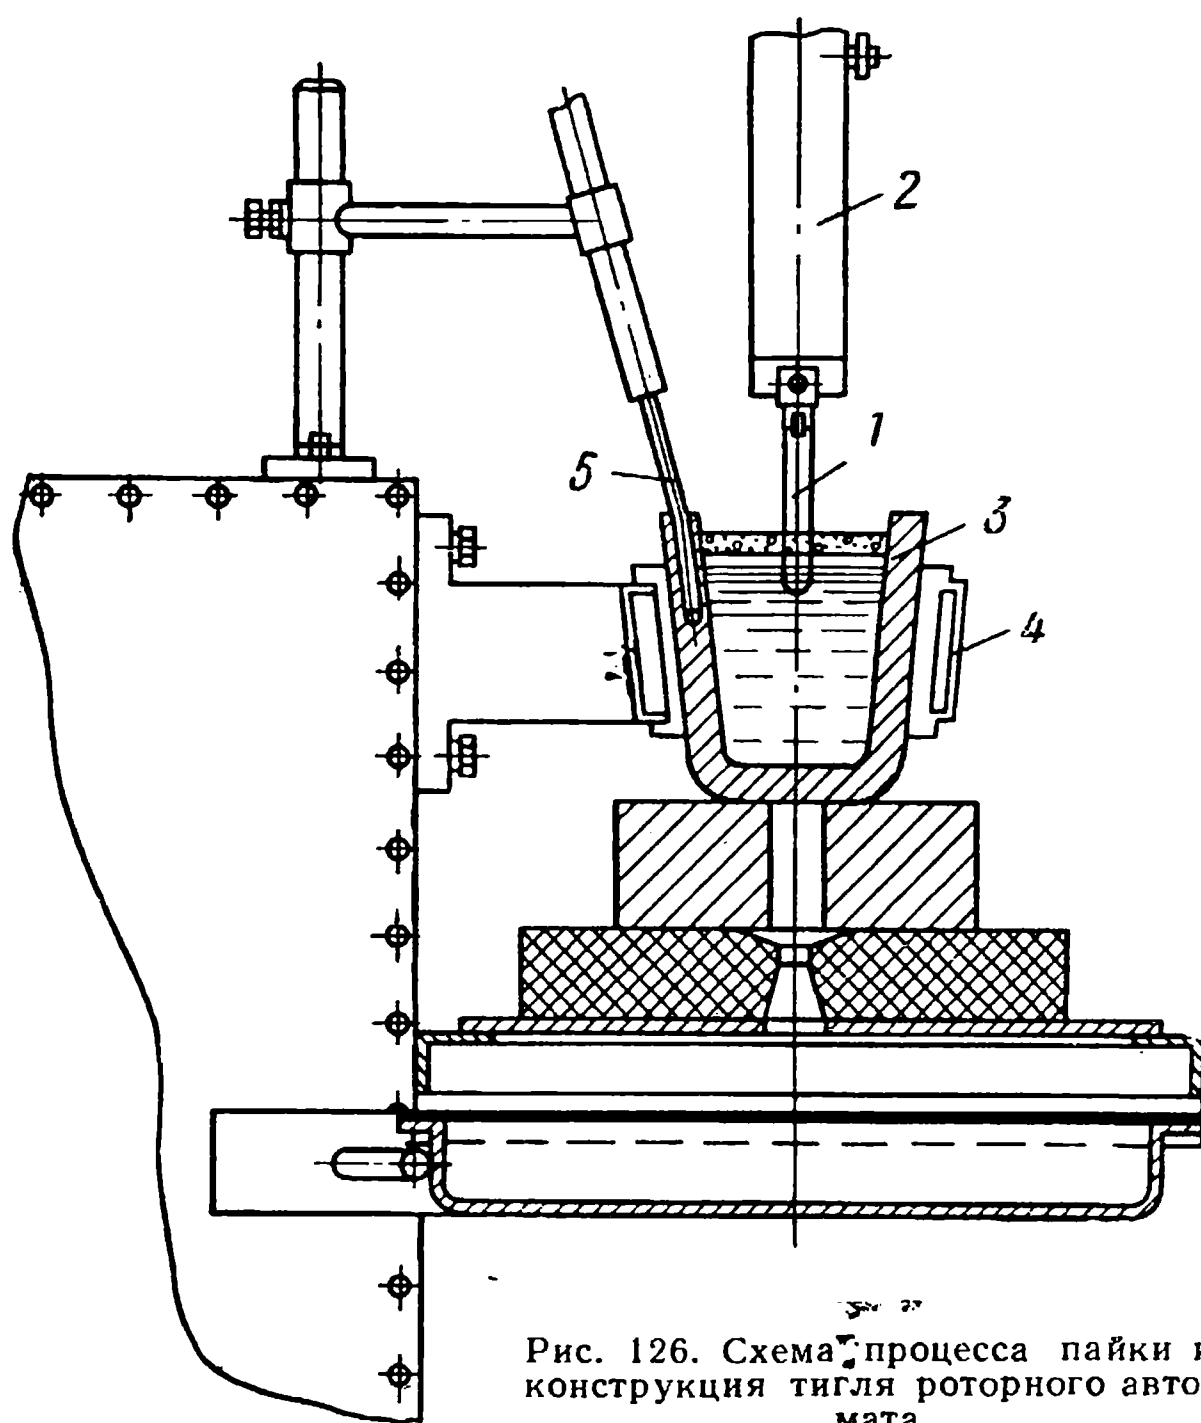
Схема процесса пайки и конструкция тигля роторного автомата
